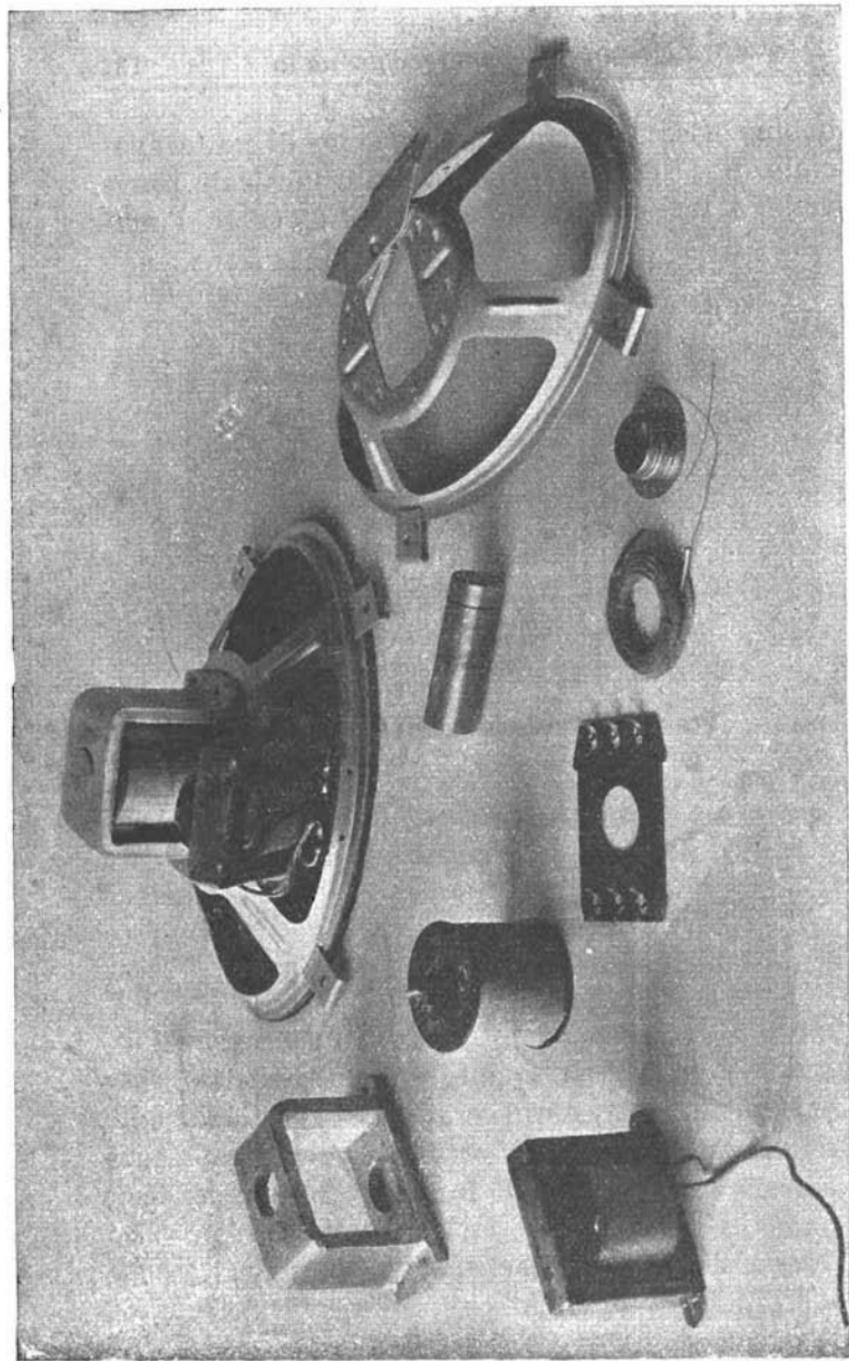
In centro ed in alto: un altoparlante. Intorno ad esso le sue parti componenti. Il cono con la bobina mobile è visibile
